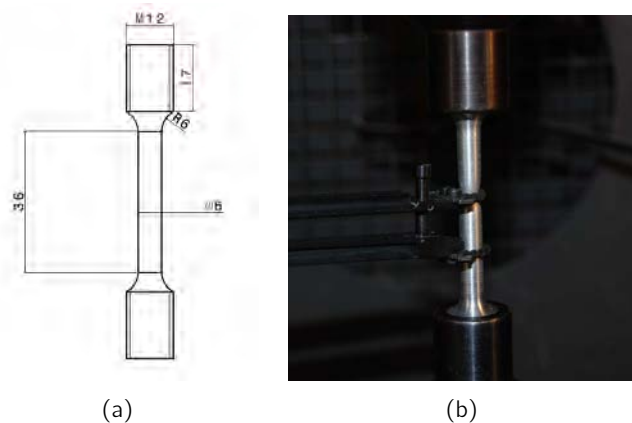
3.13(a) Dimensiones de la probeta axilsimétrica a tracción (unidades: mm), 3.13(b) Configuración inicial de los ensayos de tracción.
